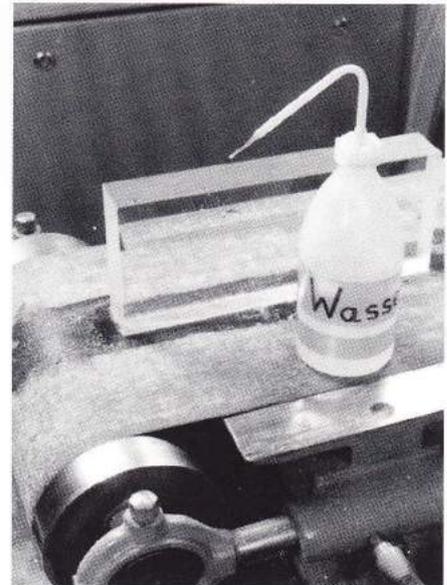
Влажная шлифовка на ленточном шлифовальном станке
